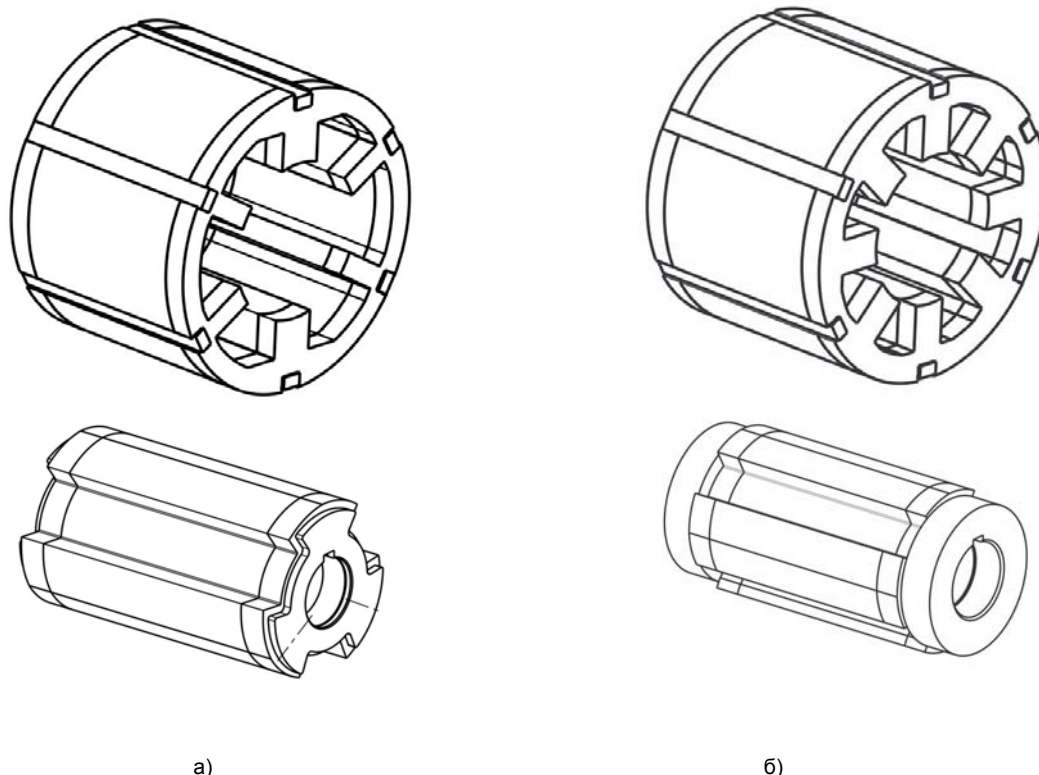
Общий вид сердечников статора и ротора ВИД: а – ВИД конструкции с $z_s/z_r = 6/3$; б – ВИД конструкции с $z_s/z_r = 4/8$
